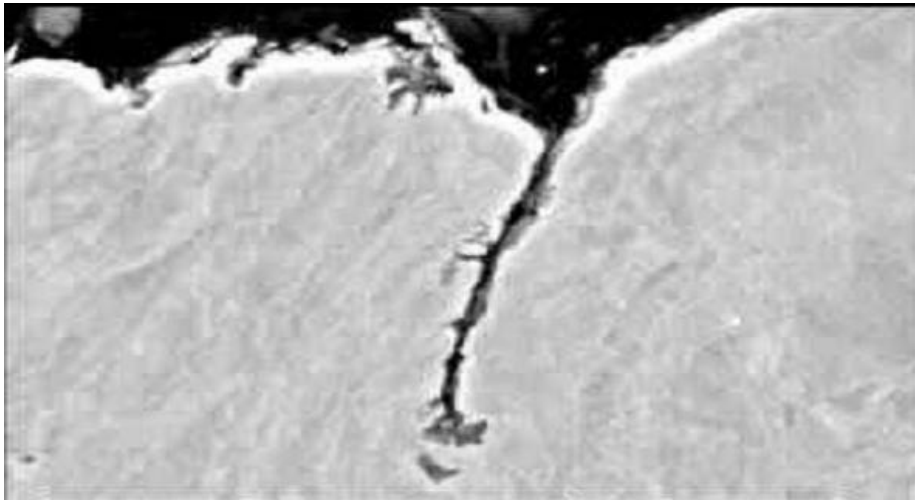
Fissure dans des joints soudés [14]
